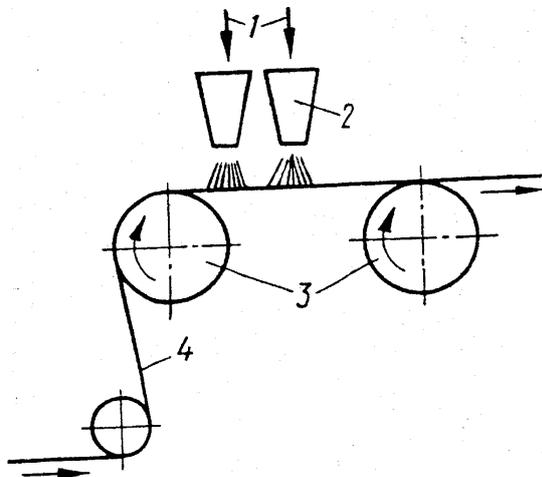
Схема фильерного разбрызгивающего устройства:
